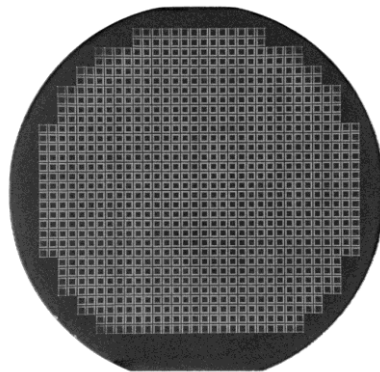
Финишная поверхность пластины кремния с дискретными квадратными зонами
